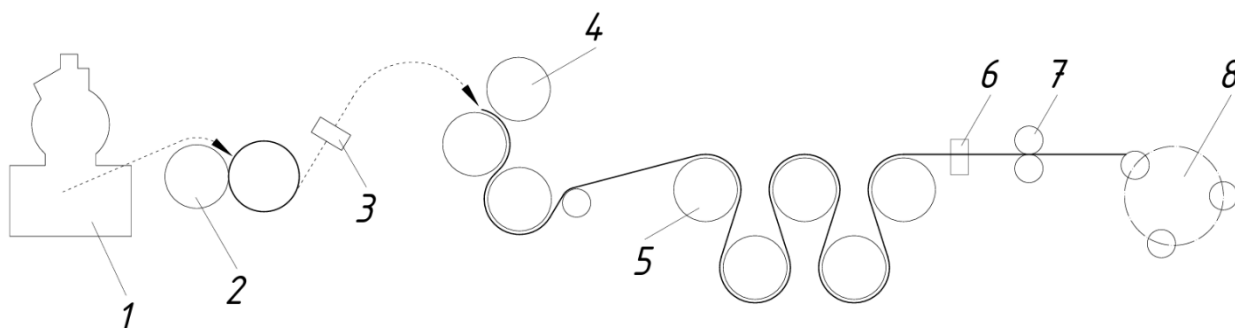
Лінія для листування гуми: 1-гумозмішувач; 2-вальці; 3-детектор металу; 4-каландр; 5-охолоджувальний пристрій; 6- контроль товщини листа; 7-механізм обрізання крайок; 8-закатний пристрій
